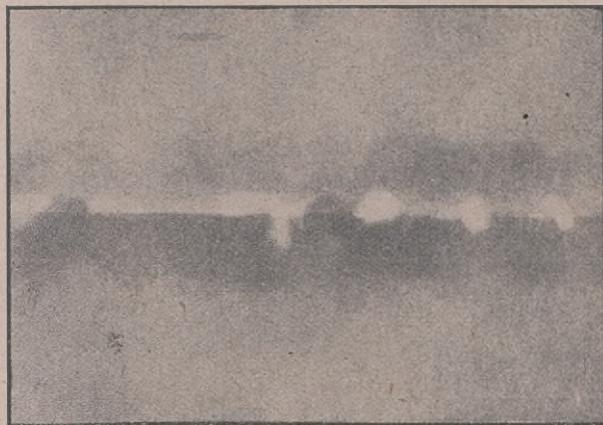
Fehlerhafte Schweißstelle bei autogener Schweißung einer 10 mm dicken Eisenplatte.
